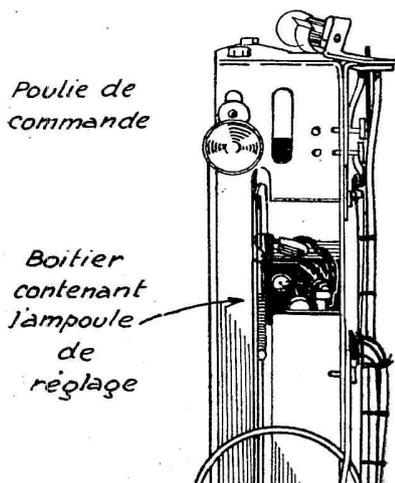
Vue arrière du boîtier de réglage visuel et du support de cadran d'un 536 Philips
